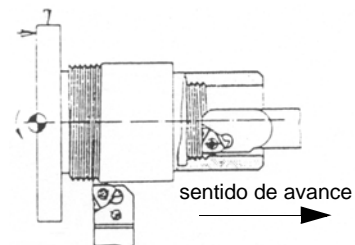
Rosca izquierda en giro derecho del husillo de máquina
